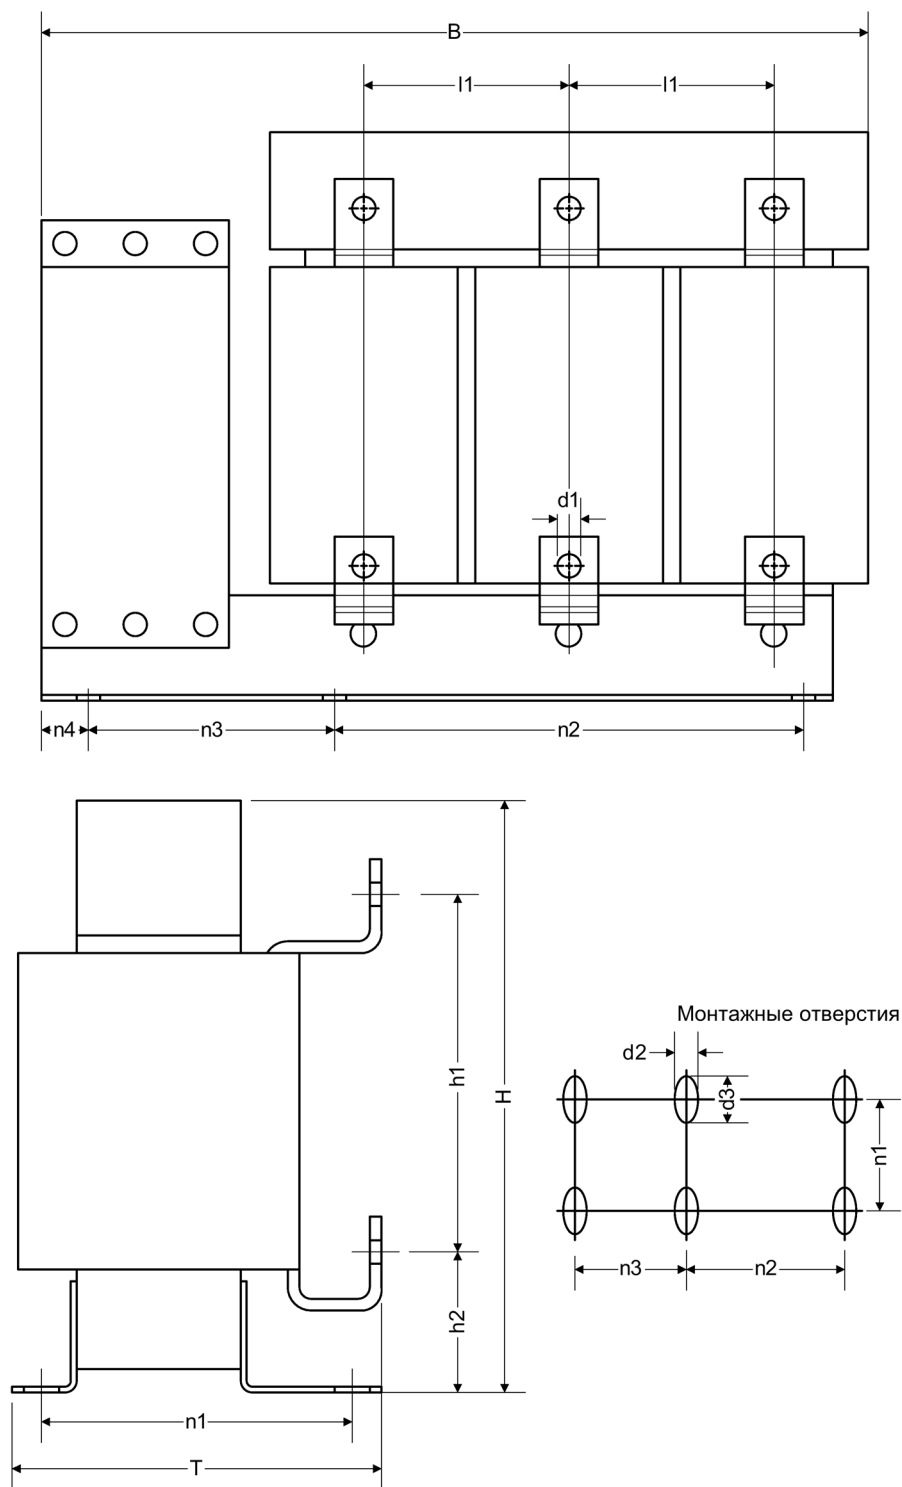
Габаритный чертёж синусоидального фильтра
